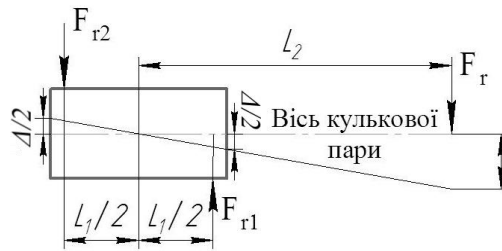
Схема для визначення довжини робочої бази гайки
